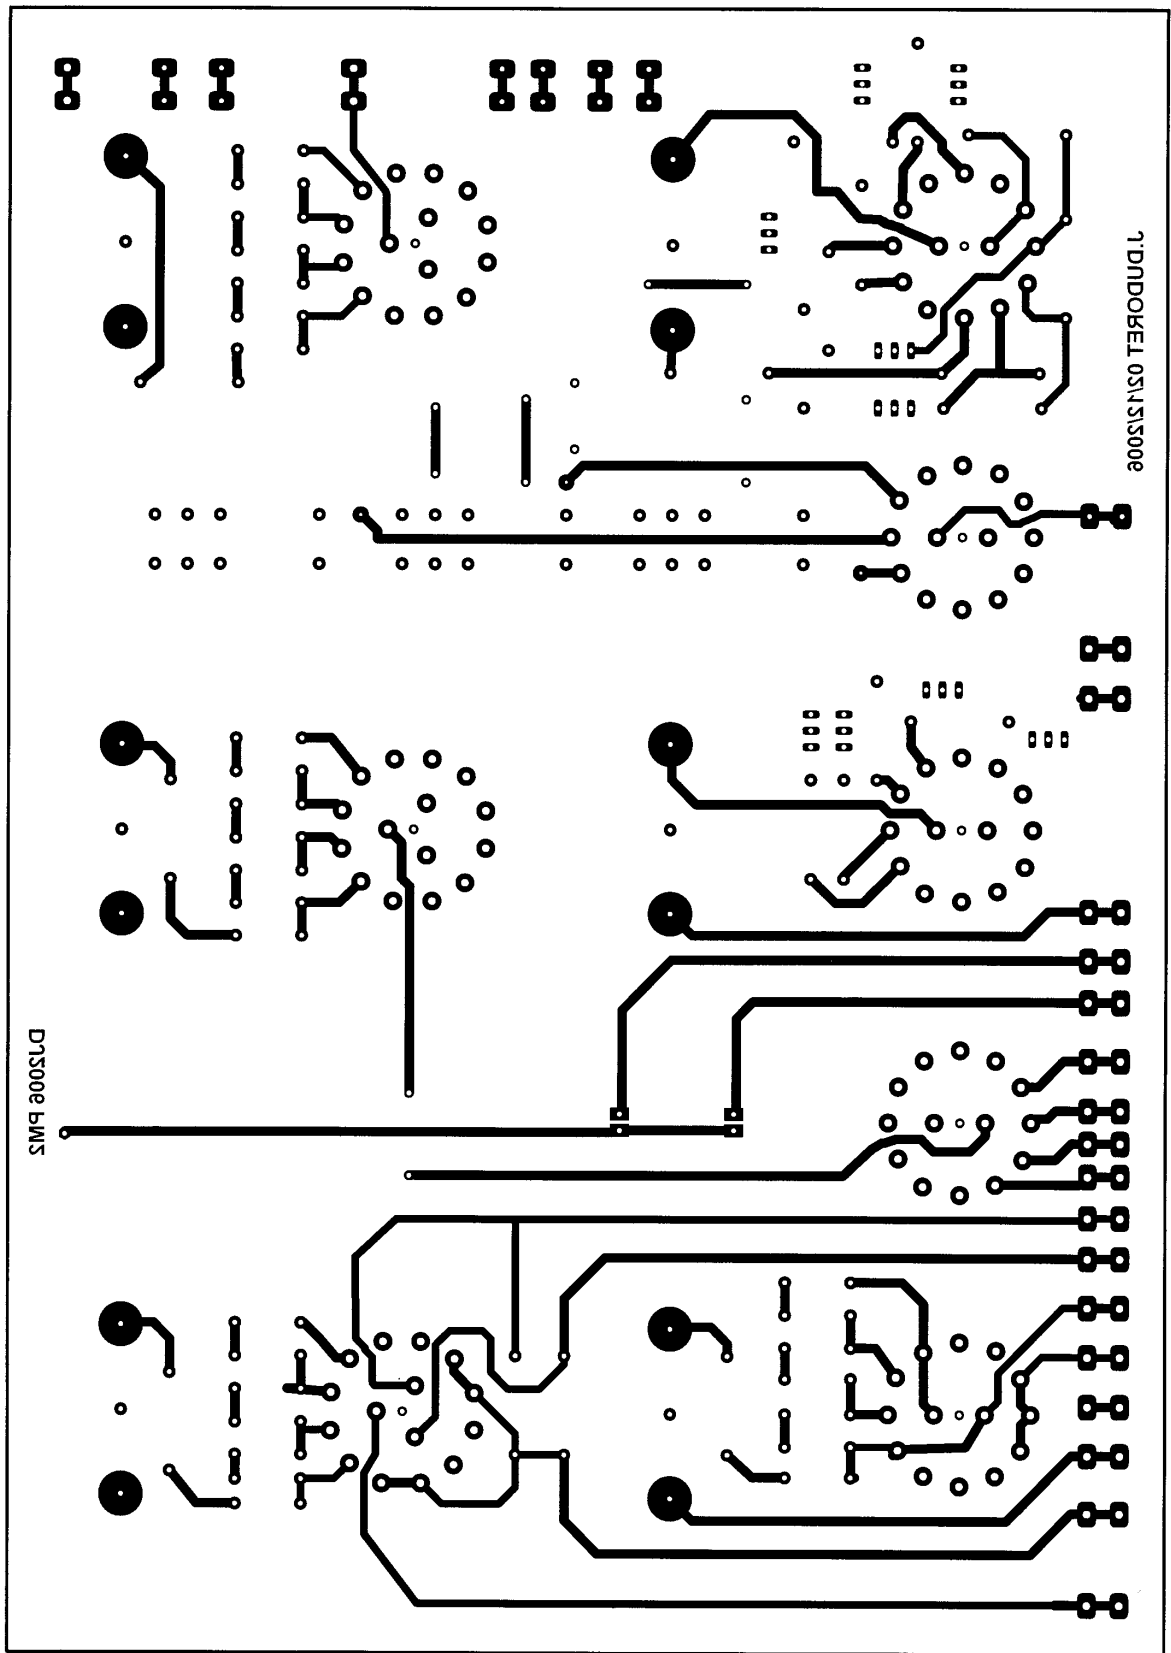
B : PCB pour 6 galvanomètres PM2 (179 x 252 mm) face B.
